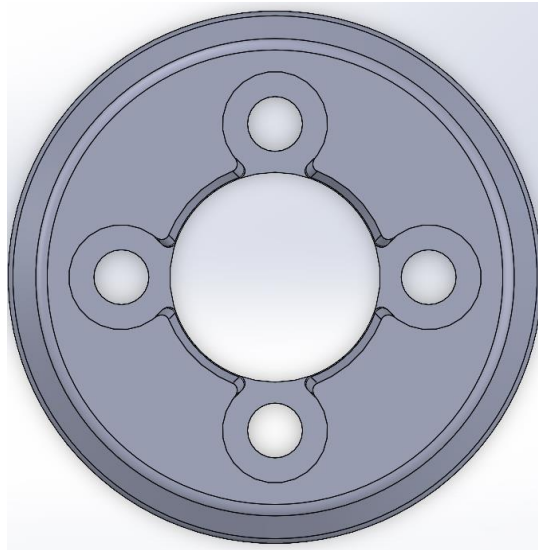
Вид зверху фіксуючої кришки шарнірного вузла з посадочними місцями під головки болтів
